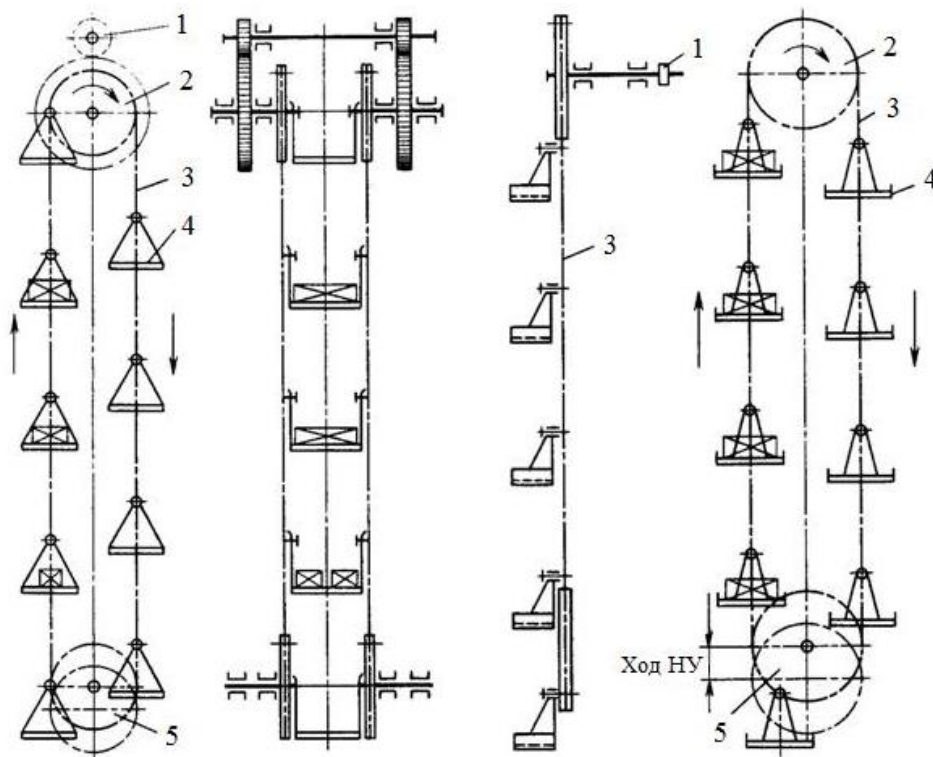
Схема люлочного элеватора (одноцепного и двухцепного):
